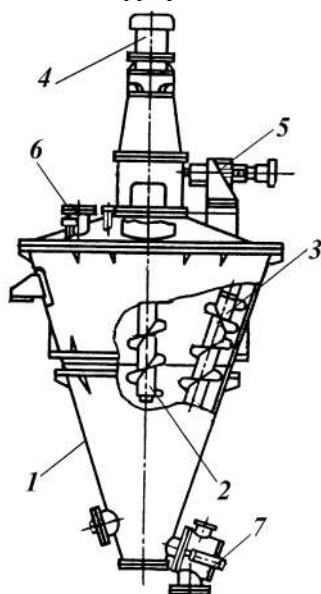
Смеситель планетарно-шнековый типа ПШ: 1 – камера; 2 – центральный шнек, 3 – наклонный шнек; 4 – привод шнеков; 5 – привод водила; 6 – загрузочный штуцер; 7 – разгрузочный клапан.
